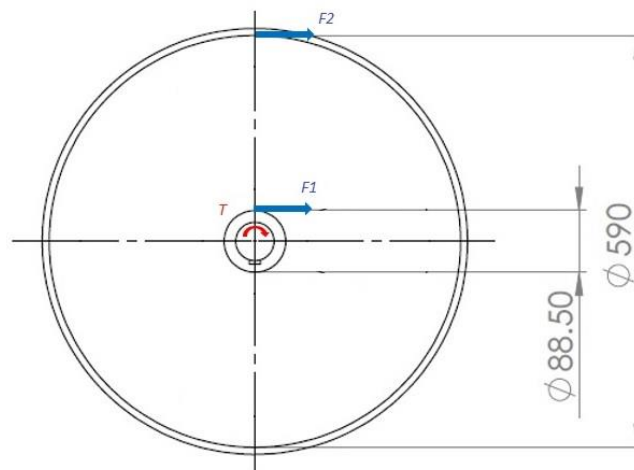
Diagrama cuerpo libre soldaduras tapa rodillo.
